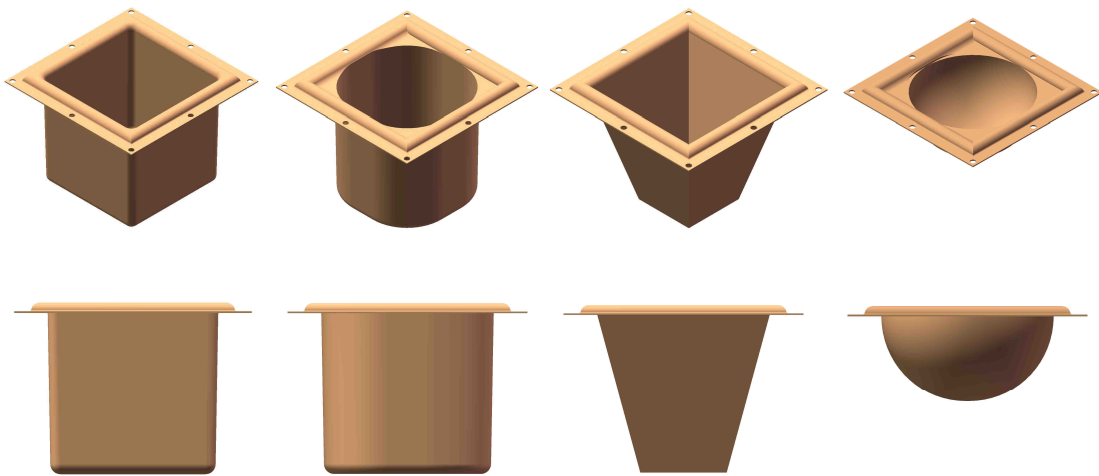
Vistas varias de diseños básicos de cavidad interior de molde de níquel de 1 mm de espesor. De izquierda a derecha, en forma cúbica, cilíndrica, tronco piramidal y semiesférica.
